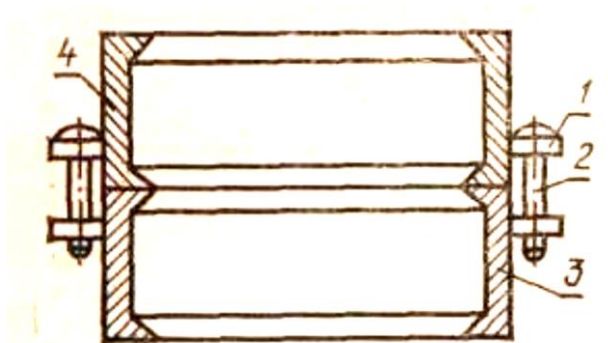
Формовочные опоки: 1 – крепёжные уши; 2 – крепёжный штырь; 3 – опока нижняя; 4 – опока верхняя
